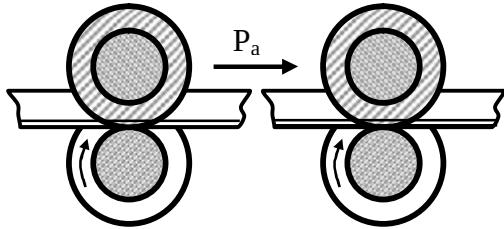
Схема создания аксиального подпора в роликах профилировочного станка
